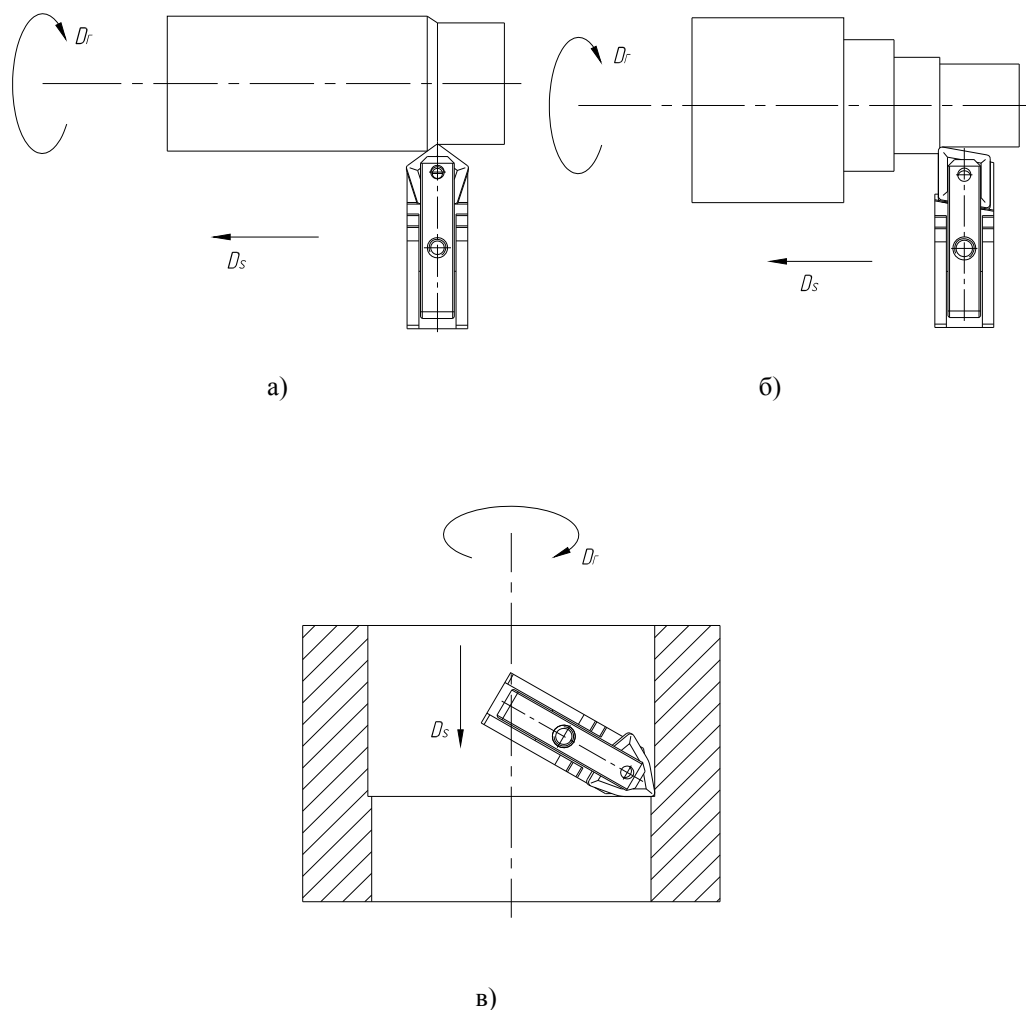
Получение унифицированным резцовым блоком: а – гладкой цилиндрической наружной поверхности; б – ступенчатой цилиндрической наружной поверхности; в – цилиндрической внутренней поверхности
